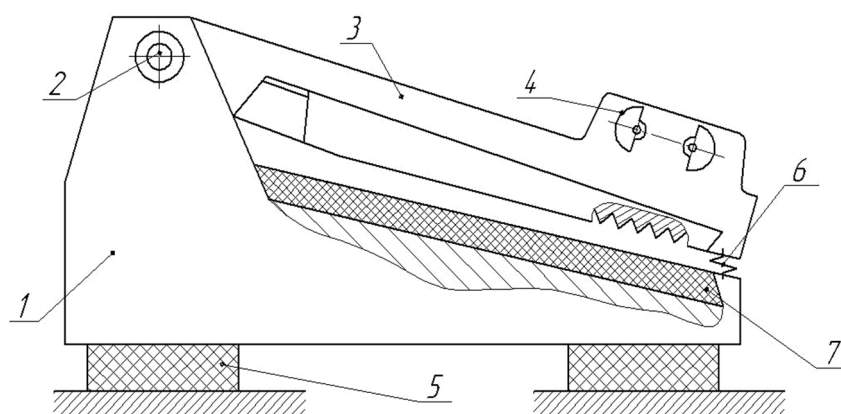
Конструктивная схема дробилки с эластомерным покрытие
